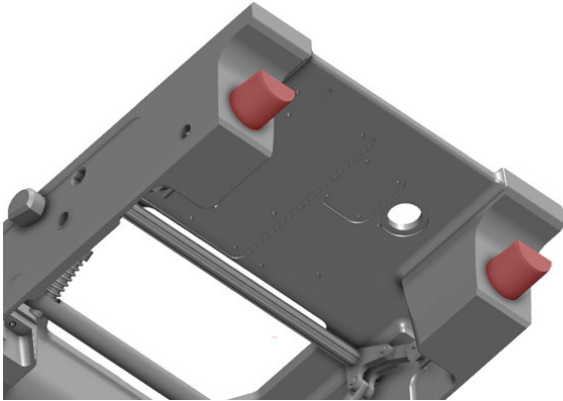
Verriegelungsmechanik und Riegelbolzen am Chassis
